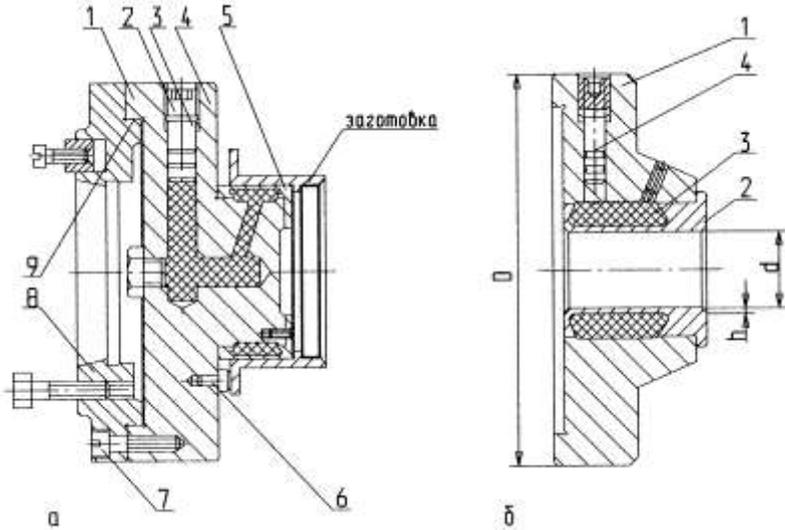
Конструкции приспособлений с гидропластмассой
